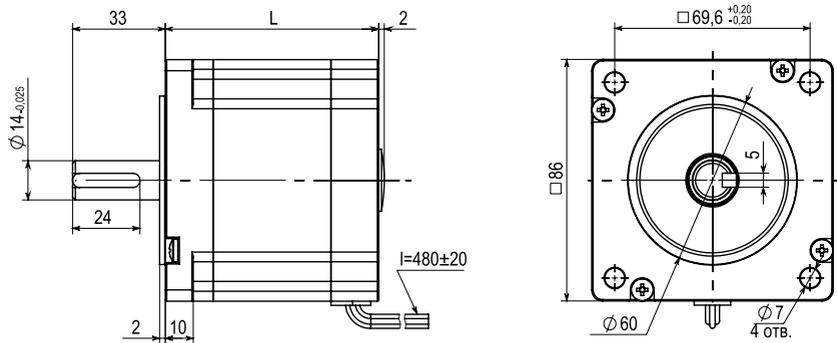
габаритные размеры шаговых двигателей серии SMO-34
